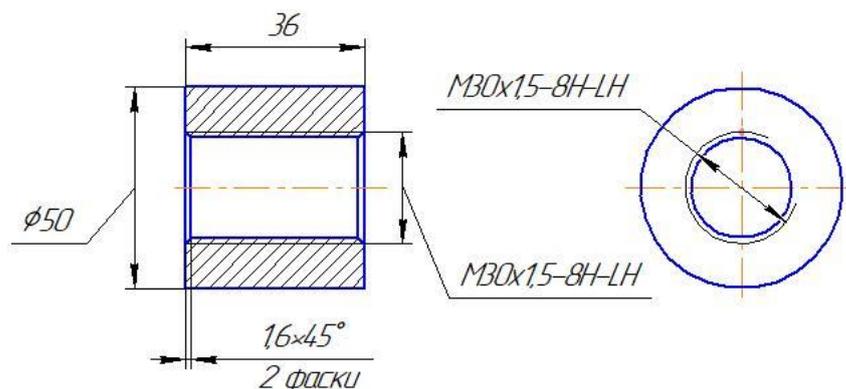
Чертеж втулки с обозначенными размерами резьбы.
